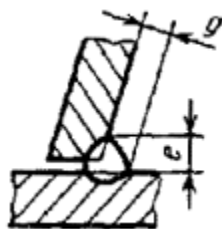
по ГОСТ 23518-79, сварной шов №1
